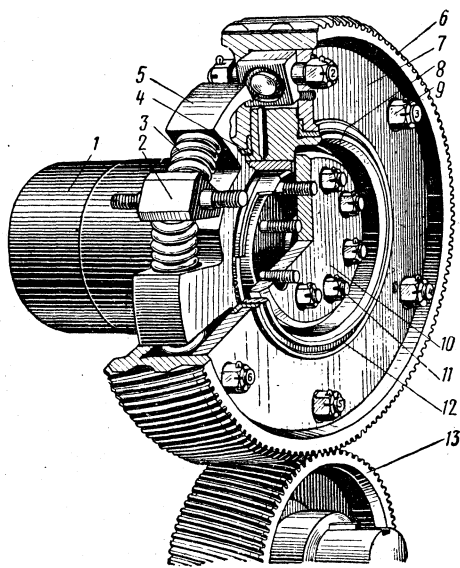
Эластичный привод воздуходувки дизеля 2Д100:
